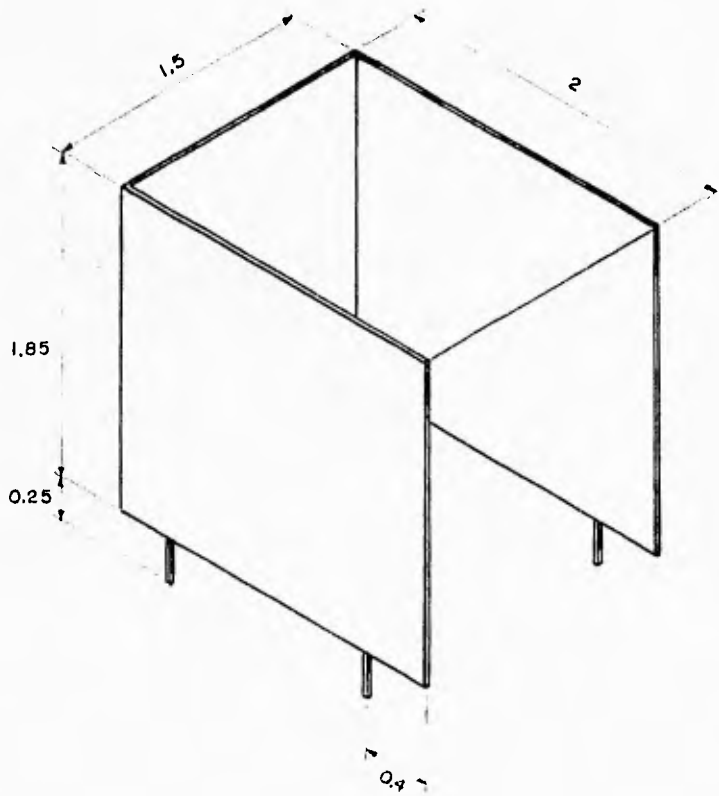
3a. propuesta para el taller de soldadura
